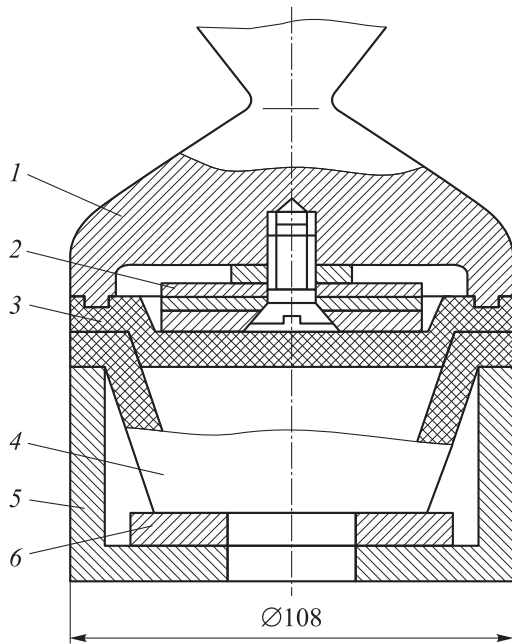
Схема сварки полиэтиленовой банки контурным волноводом:
